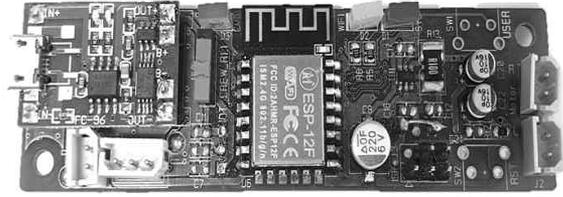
반려 동물 돌봄 로봇의 PCB 기판
